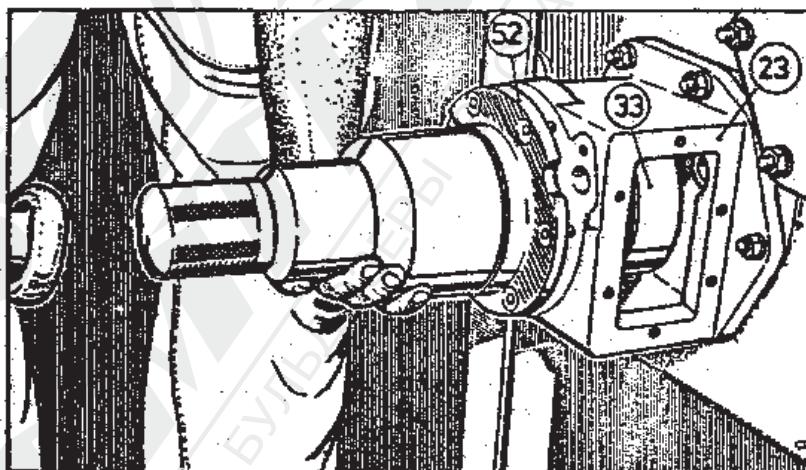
Вдавливание узла держателя 52 с подшипником и валиком в корпус 23 с одновременным вдавливанием гнезда валика привода заднего моста /33 - см. рис. 2-20/ на шарикоподшипник 6213.
